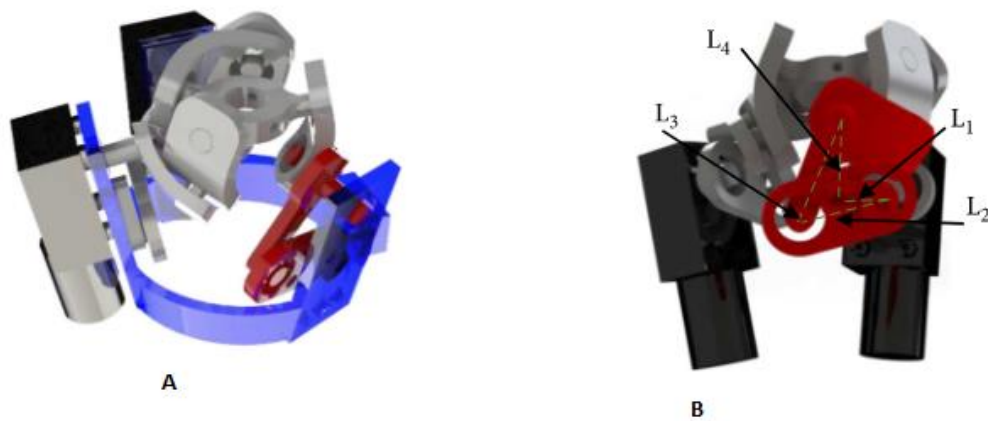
Um projeto CAD do manipulador paralelo final com os mecanismos de quatro barras: (a) vista isométrica; (b) vista frontal.
